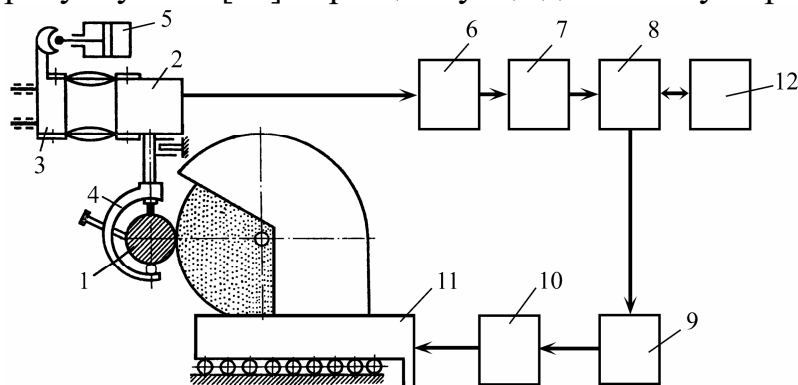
Схема пристрою автоматизованого контролю заготовки під час обробки: 1 – заготовка; 2 – датчик; 3 – підвіска; 4 – скоба; 5 – гідроциліндр переміщення підвіски; 6 – перетворювач; 7 – підсилювач; 8 – блок порівняння; 9 – пристрій керування; 10 – привод подачі; 11 – шліфувальна бабка; 12 – пристрій задання
